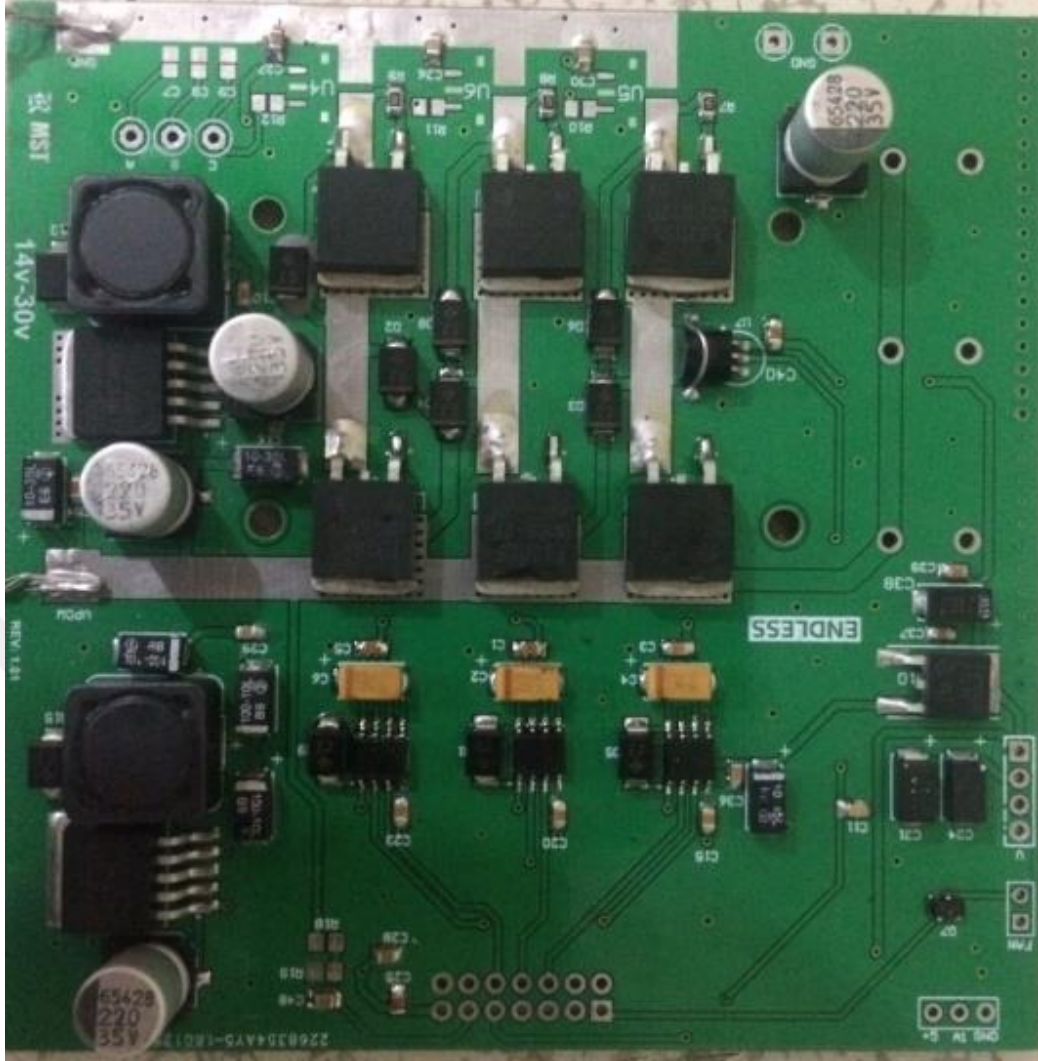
Üç boyutlu PCB (arka taraf)
